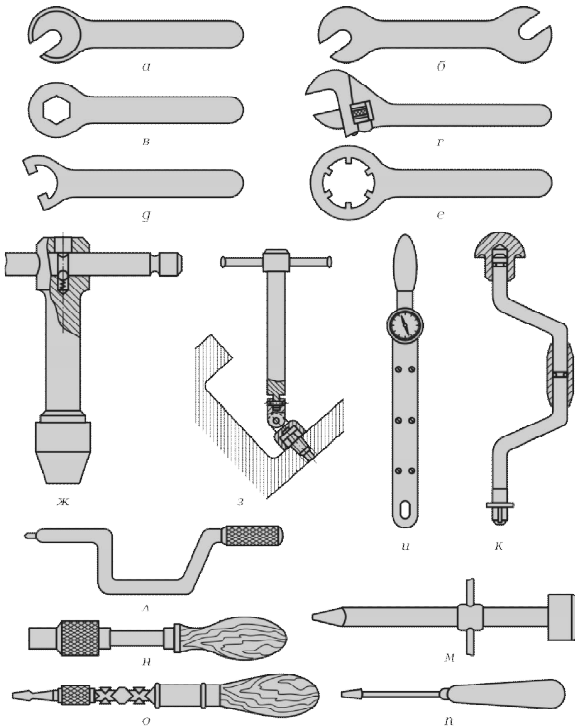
Ручний інструмент для складання різьбових з'єднань:
